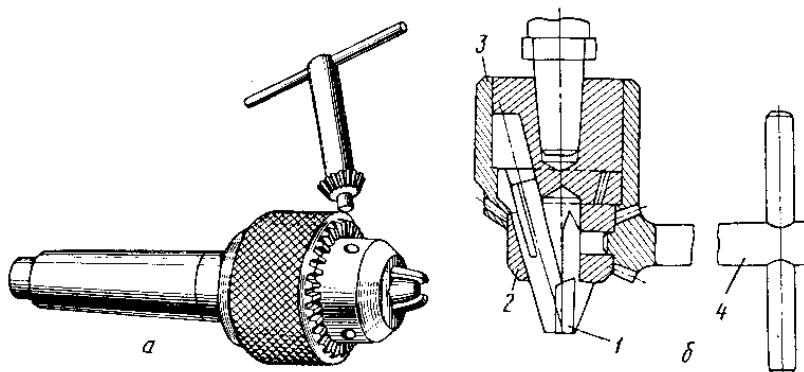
Патрон для крепления осевого инструмента: а – общий вид;
